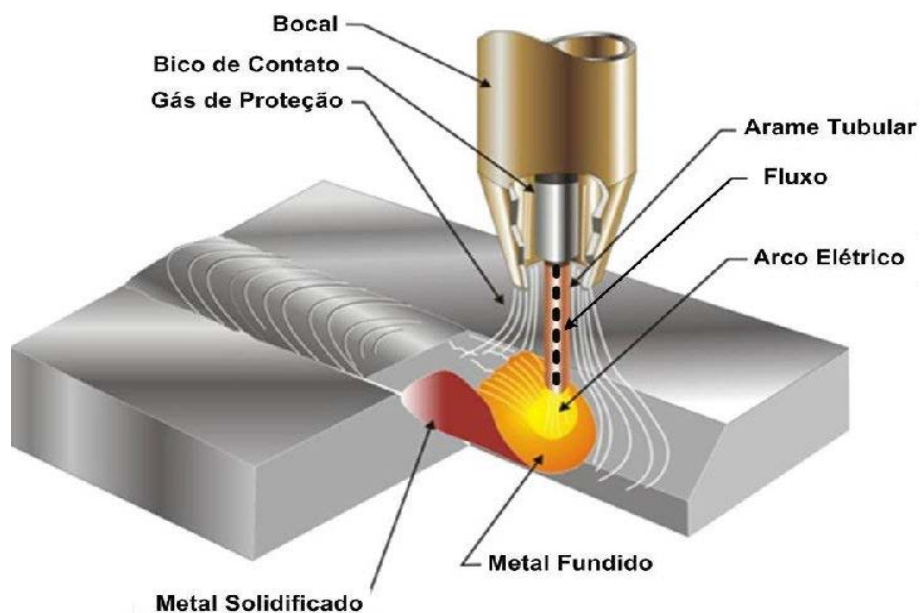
Ilustração do processo de soldadura FCAW com proteção gasosa [17].
